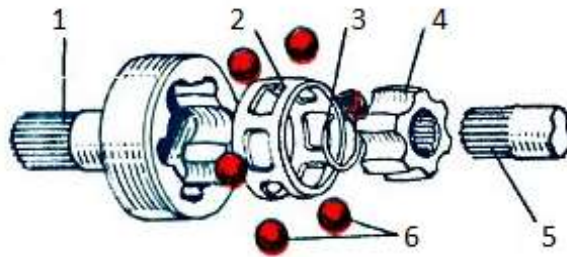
Кульковий шарнір зі зміщеними ділильними канавками типу «Рцеппа-Бірфільд» [6]:
